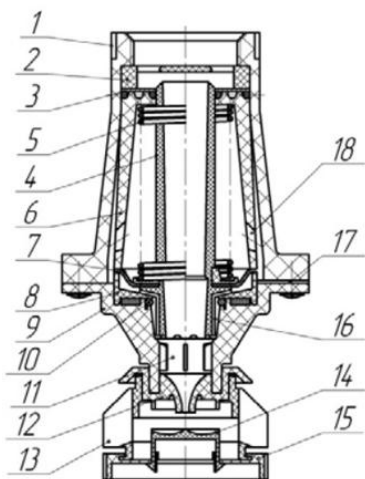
Вид насадки постоянного расхода: 1 – корпус; 2 – кольцо; 3 – шайба; 4 – трубка; 5 – пружина; 6 – вставка; 7 – мембрана; 8 – манжета; 9 – основание; 10 – кольцо; 11 – ребра; 12 – сопло; 13 – стойка; 14 – дефлектор; 15 – гайка; 16 – зазор; 17 – щель; 18 – отверстие.
